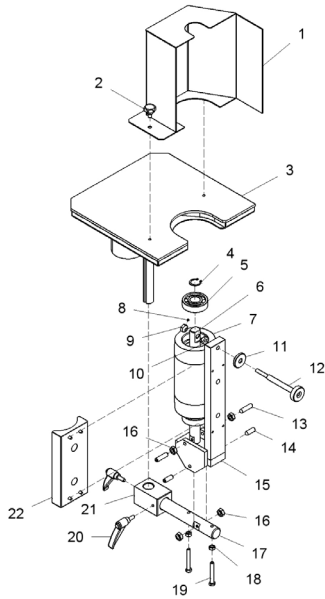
Ersatzteilzeichnung 5 Schwenkmechanismus
